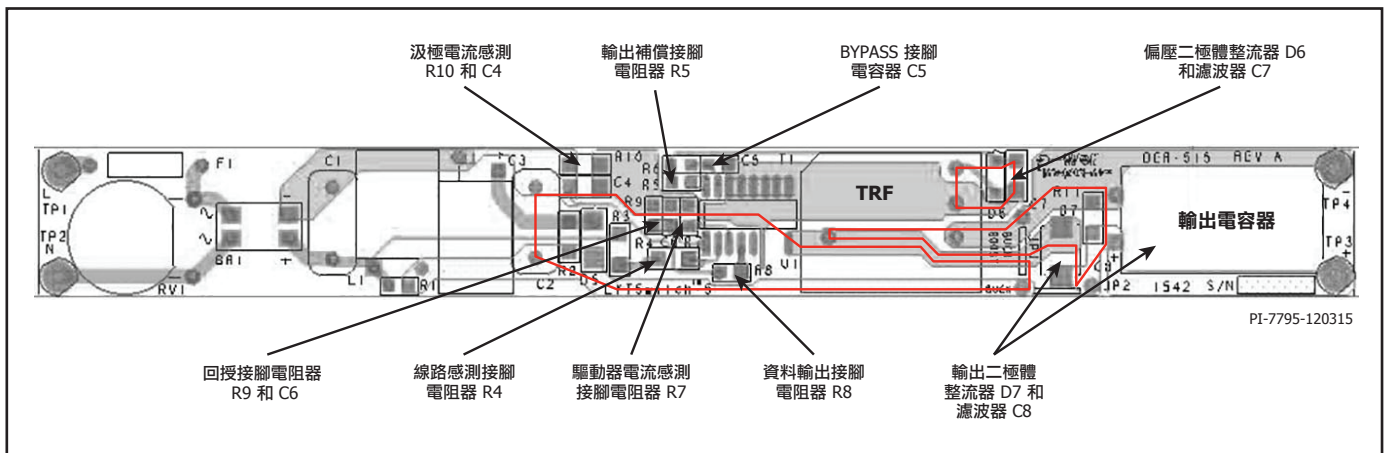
採用 SO-16B D 封裝的 DER-515 PCB 佈局範例顯示 PCB 佈局中關鍵元件的位置和迴路面積
